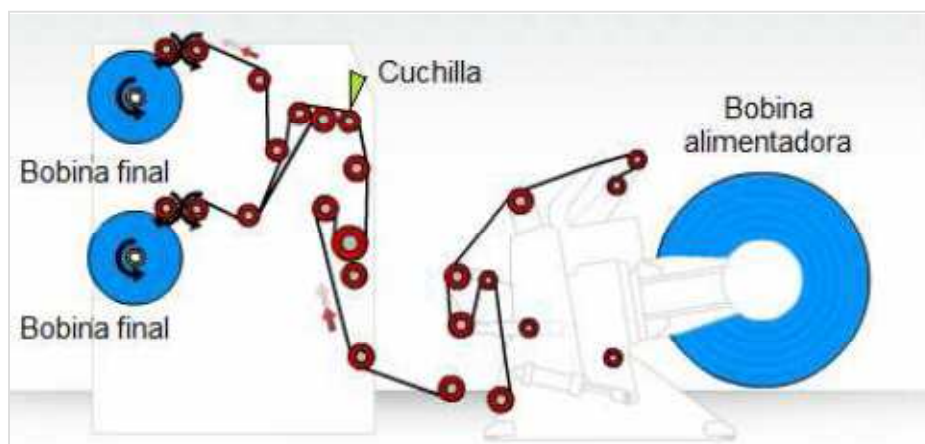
Esquema de una máquina cortadora rebobinadora³
